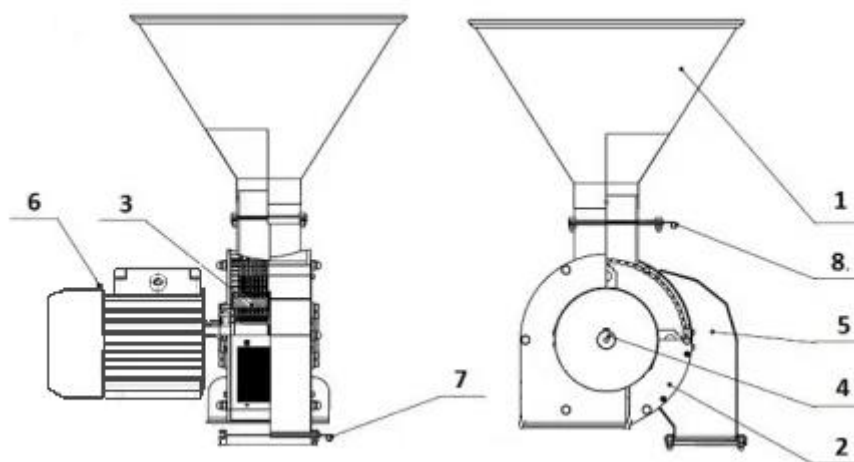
Бытовая дробилка: 1 –зерновой бункер; 2 - корпус кормоизмельчителя, 3 – ротор; 4 - вал; 5 – выгружающий бункер; 6 – электродвигатель; 7 – регулировочная заслонка для выгрузки зерна; 8 – регулировочная заслонка для подачи зерна.
